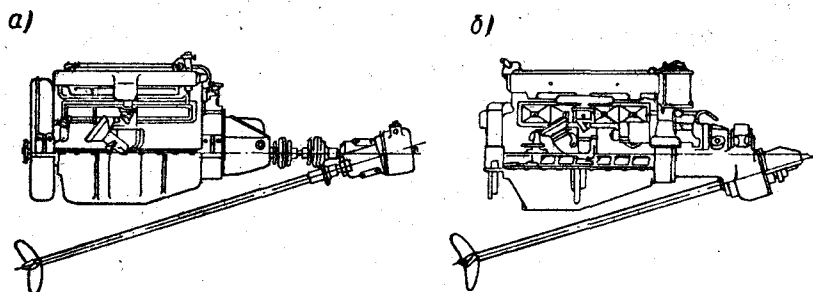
Два вида углового редуктора для стационарного двигателя: а — с коротким промежуточным карданным валом; б — закрепленный на двигателе.
